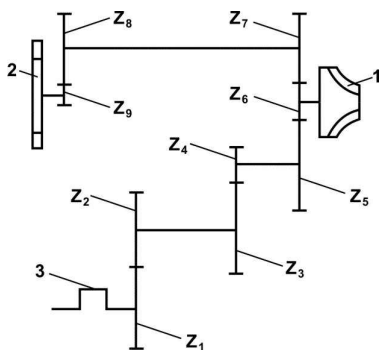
Кінематична схема приводу компресора дизеля ЗТД-3А:
